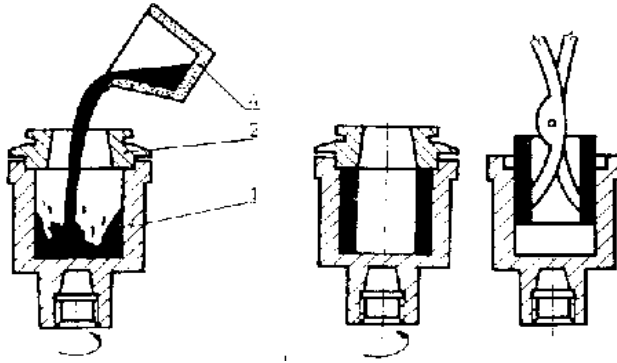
Schleuderguss mit vertikaler Drehachse
